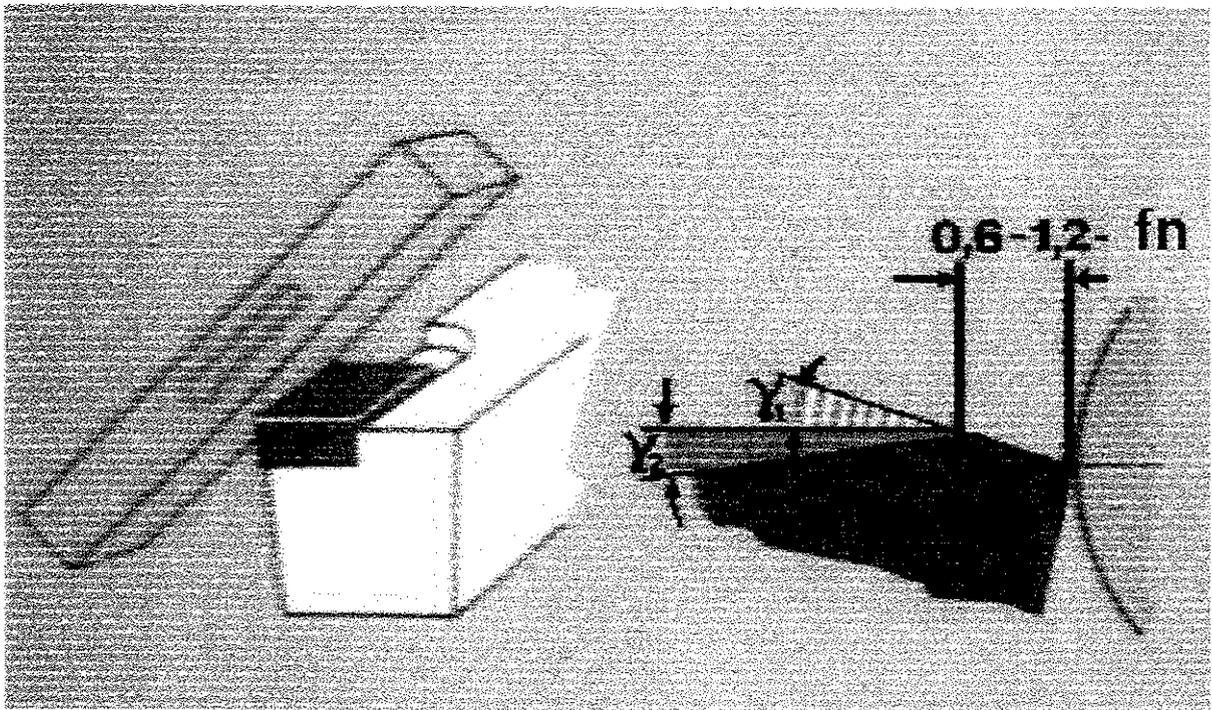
Exemplo de chanfro de aresta para ferramenta soldada
